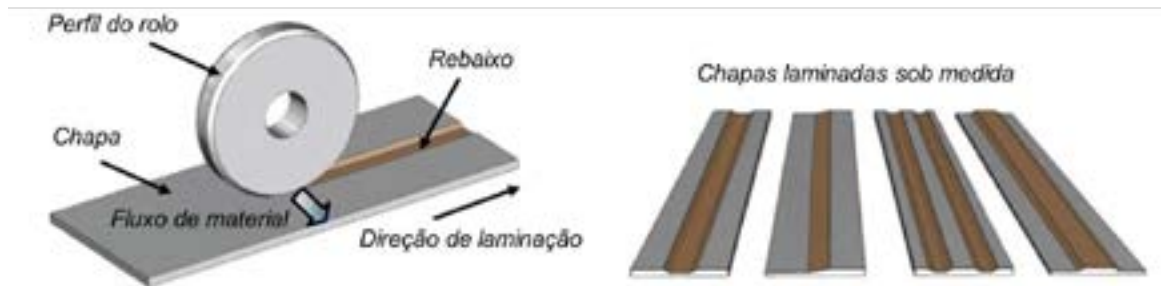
Desenho esquemático do processo de laminação flexível e diferentes estruturas TRB [17].
